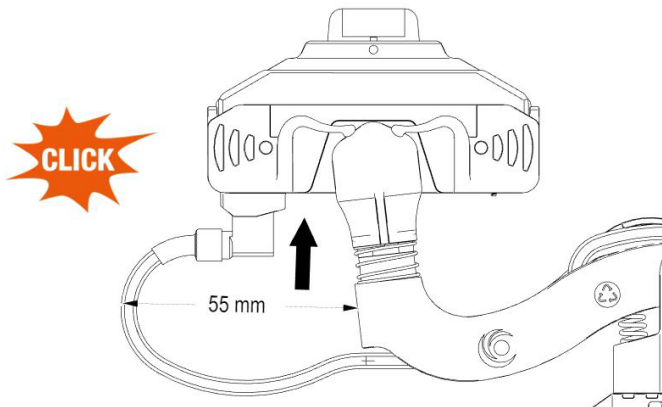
Gewinkelte Flachsteckhülse aufstecken
